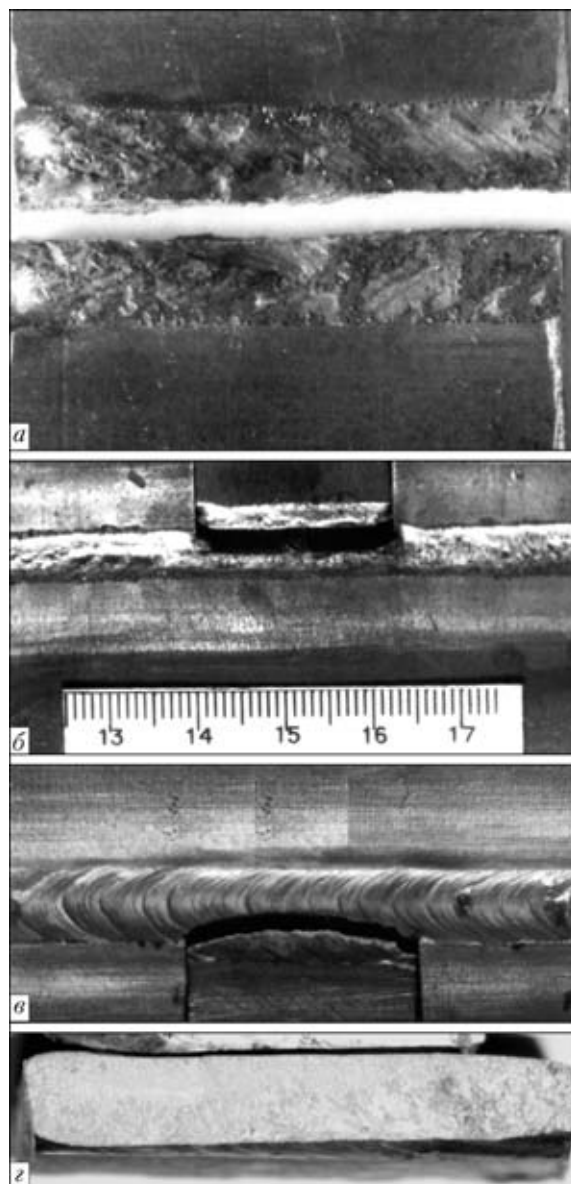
Внешний вид и расположение изломов замедленного разрушения образцов соединений, сваренных за два прохода без (а, б) и с усилением шва (в) без (а) и с искусственными концентраторами напряжений (б, в); з — поверхность излома
